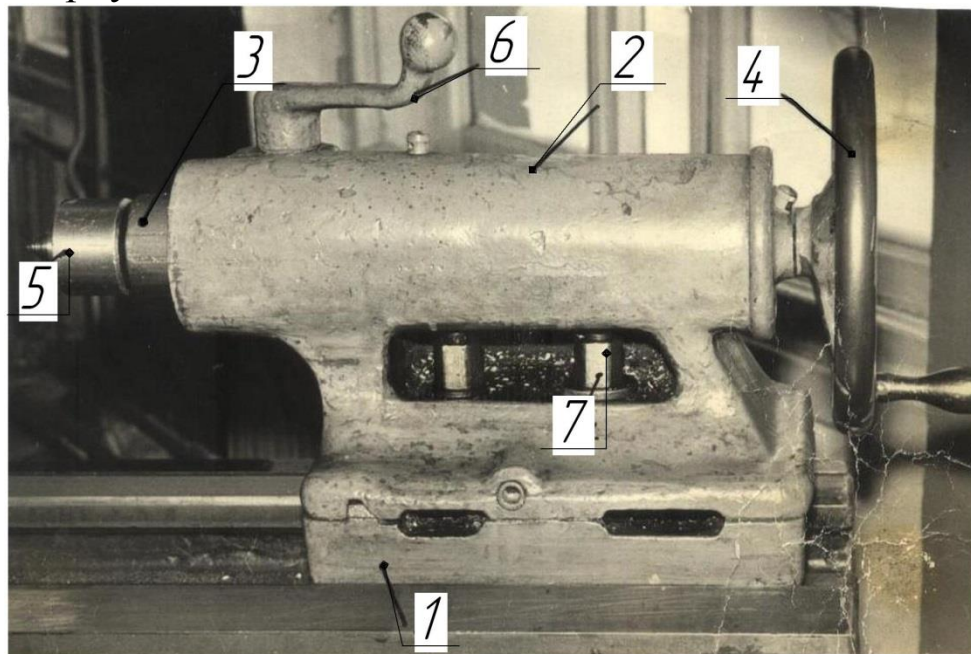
Задняя бабка (общий вид): 1 – плита; 2 – корпус; 3 – пиноль; 4 – маховичок перемещения пиноли; 5 – центр; 6 – рукоятка; 7 – болт с гайкой
